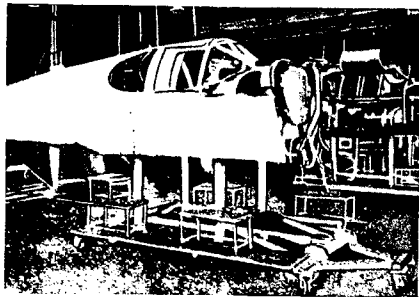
Стационарное приспособление для сборки верхней панели фюзеляжа
